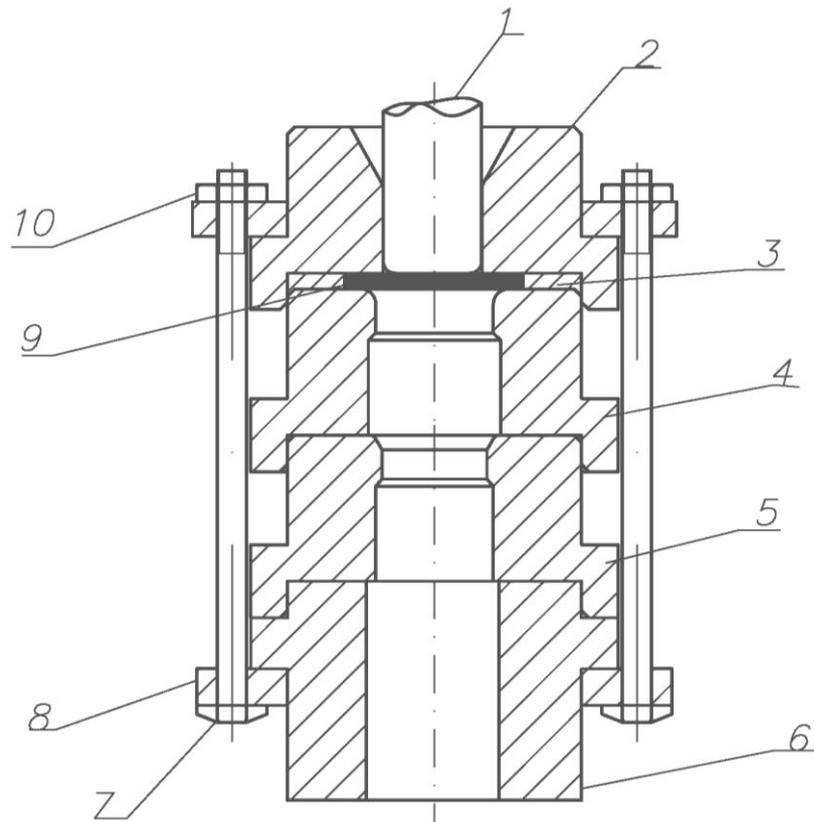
Чертеж вытяжного штампа: 1 – пуансон; 2 – верхняя часть штампа; 3 – прижимное кольцо; 4,5 – матрицы; 6 – нижняя часть штампа; 7 – стяжные болты; 8 – прокладки; 9 – заготовка; 10 – гайки
